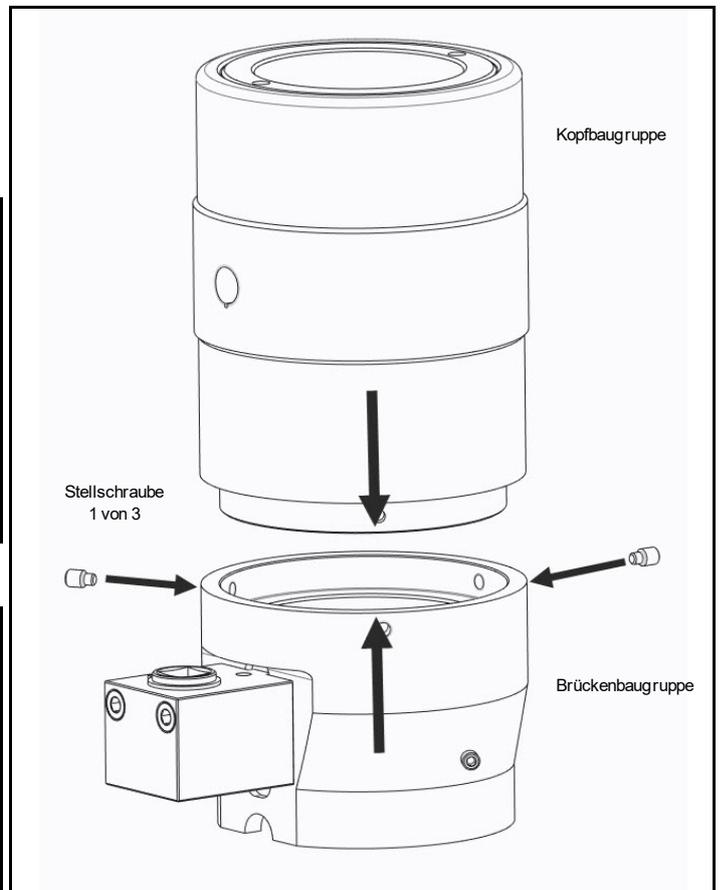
Die Kopfbaugruppe auf die Brückenbaugruppe aufsetzen und mit Gewindestiften sichern
